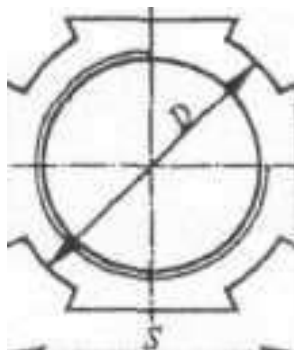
Гайки установочные заземляющие: D – диаметр гайки
